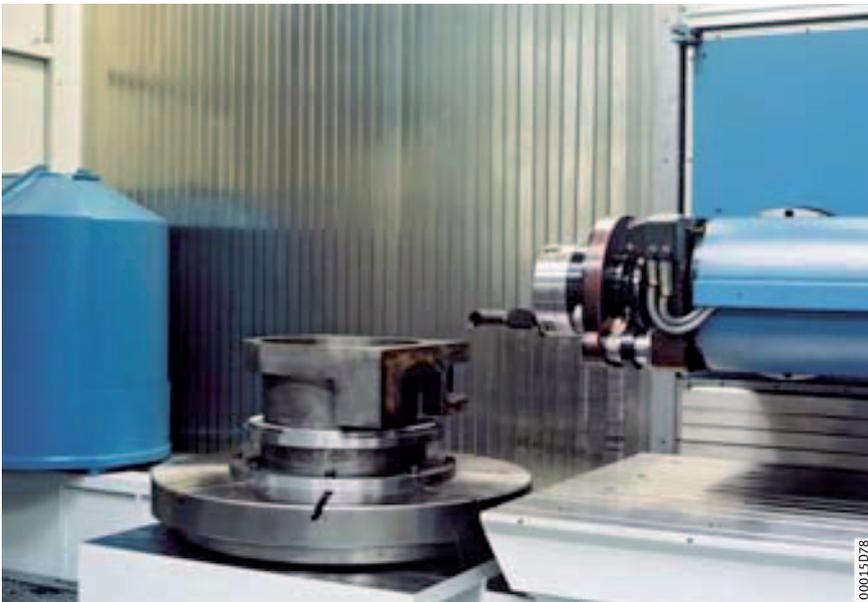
Rundtisch für Dreh-/Fräsbearbeitung in einer einzigen Aufspannung
